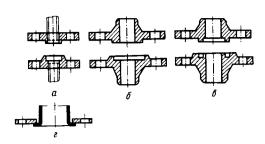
Фланцы плоские стальные: а — приварные встык (воротниковые) с выступом и впадиной; б, в — приварные встык с шипом и пазом: г — свободновращающиеся
